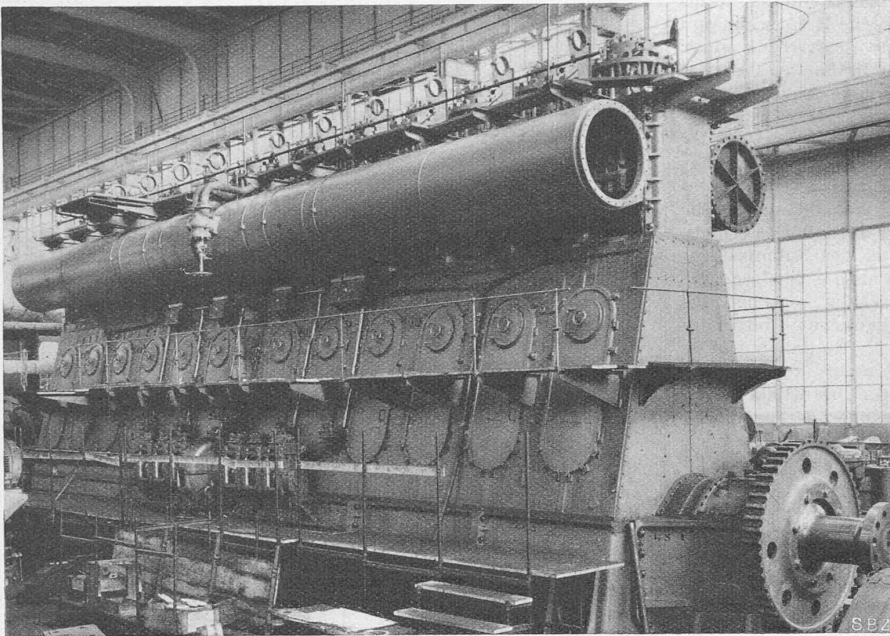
Eine der drei Hauptmaschinen für M. S. «Oranje» während der Montage
